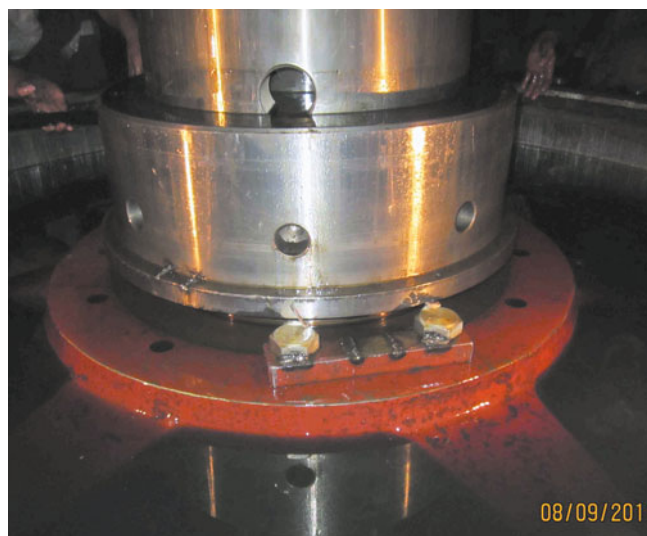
Гайка поршня сервомотора рабочего колеса ГА-1
